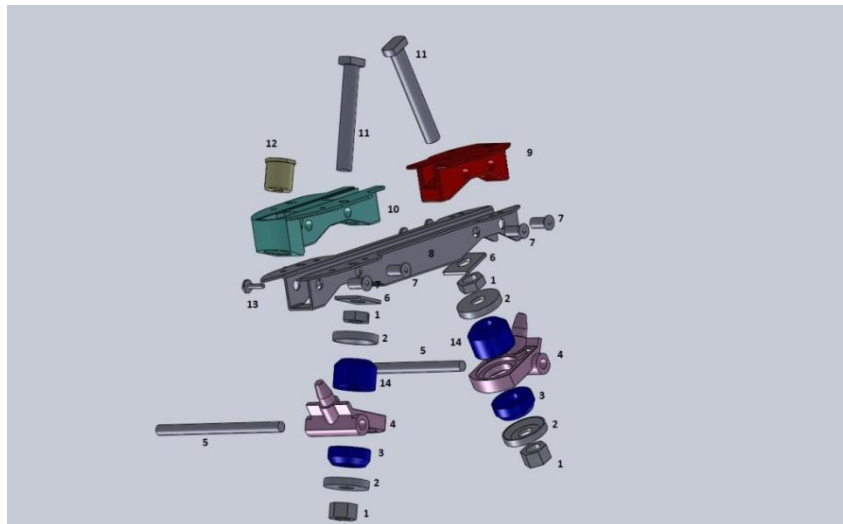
Vista explodida dos componentes do patim em chapa quinada
